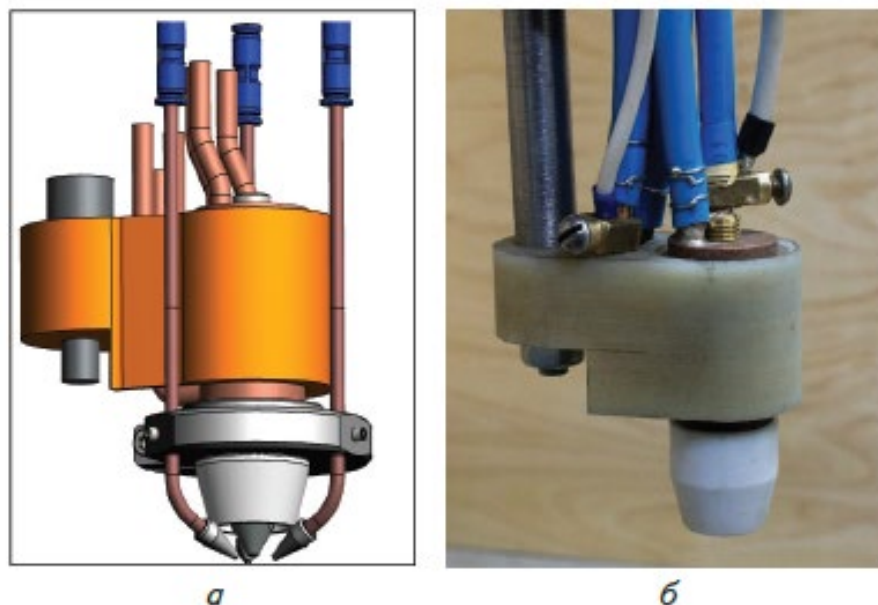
Плазмотрон установки для 3D-друку: а - комп'ютерна 3D-модель; б – загальний вигляд
